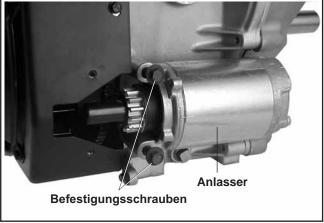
Anlasserbefestigung mit Schrauben.
